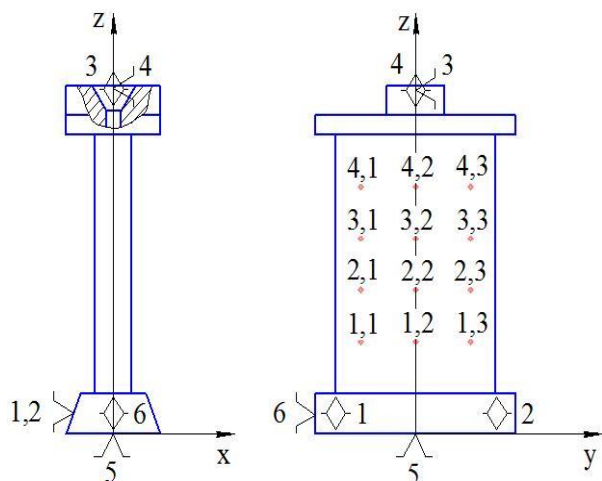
Схема базирования заготовки лопатки на операции обработки пера
